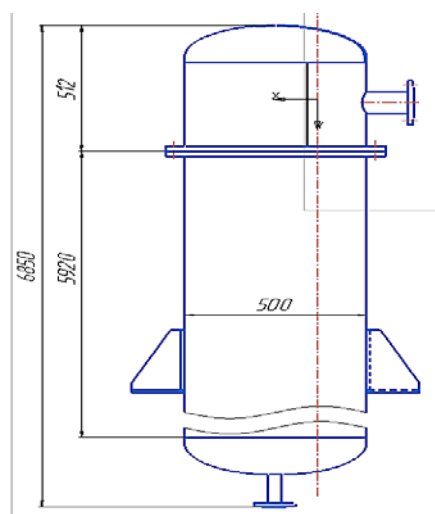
Габаритные размеры сварной конструкции «Кожухотрубный теплообменник»
